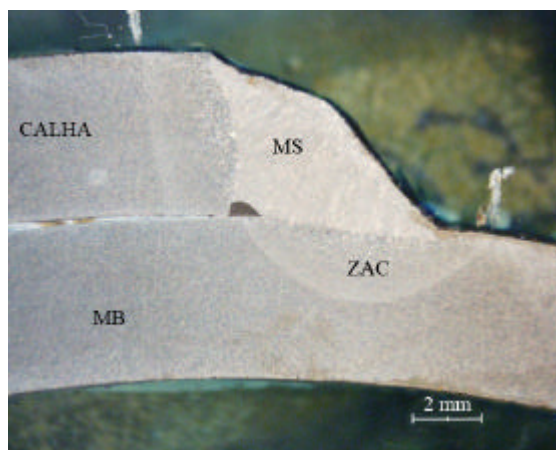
Falta de penetração observada na soldagem de filete entre calha e duto.
